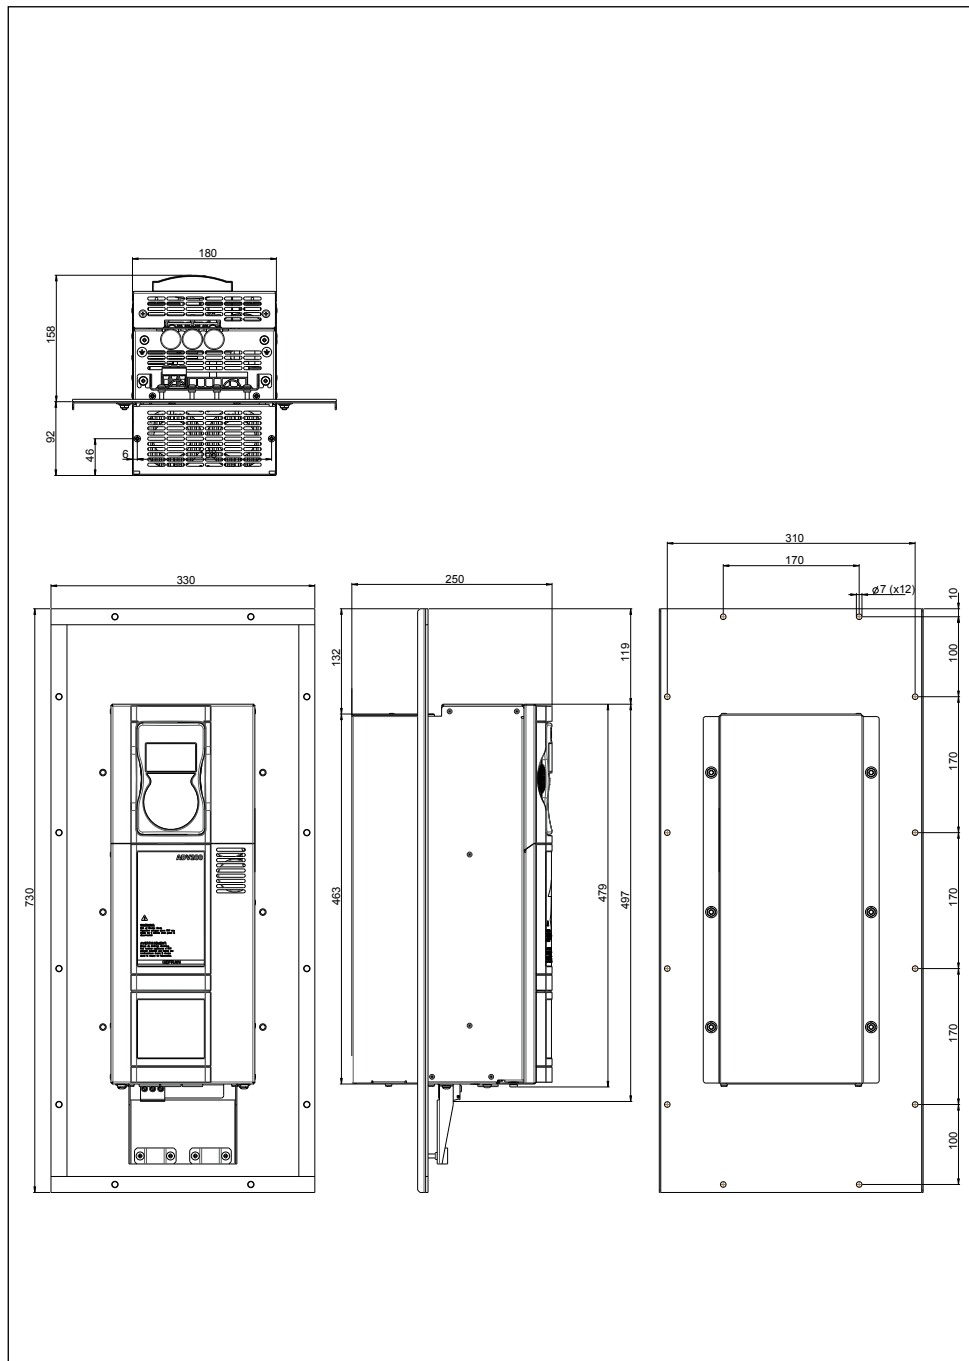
Размеры для типоразмера 4 (ADV200-...-EH)
